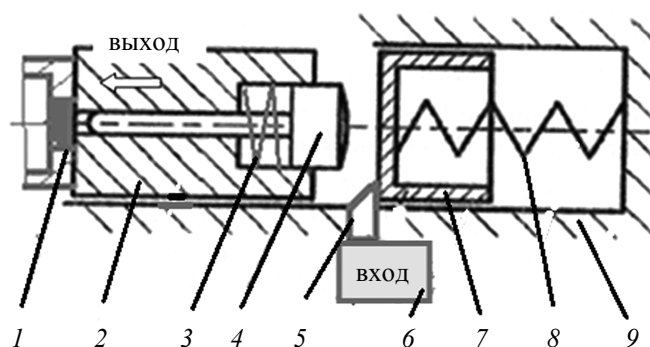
Схема ударного механизма куркового типа: 1 – капсюль-воспламенитель; 2 – затвор с направляющей ударника; 3 – пружина отбоя; 4 – ударник с бойком; 5 – шептало; 6 – спусковой механизм; 7 – курок; 8 – боевая пружина; 9 – направляющая курка
